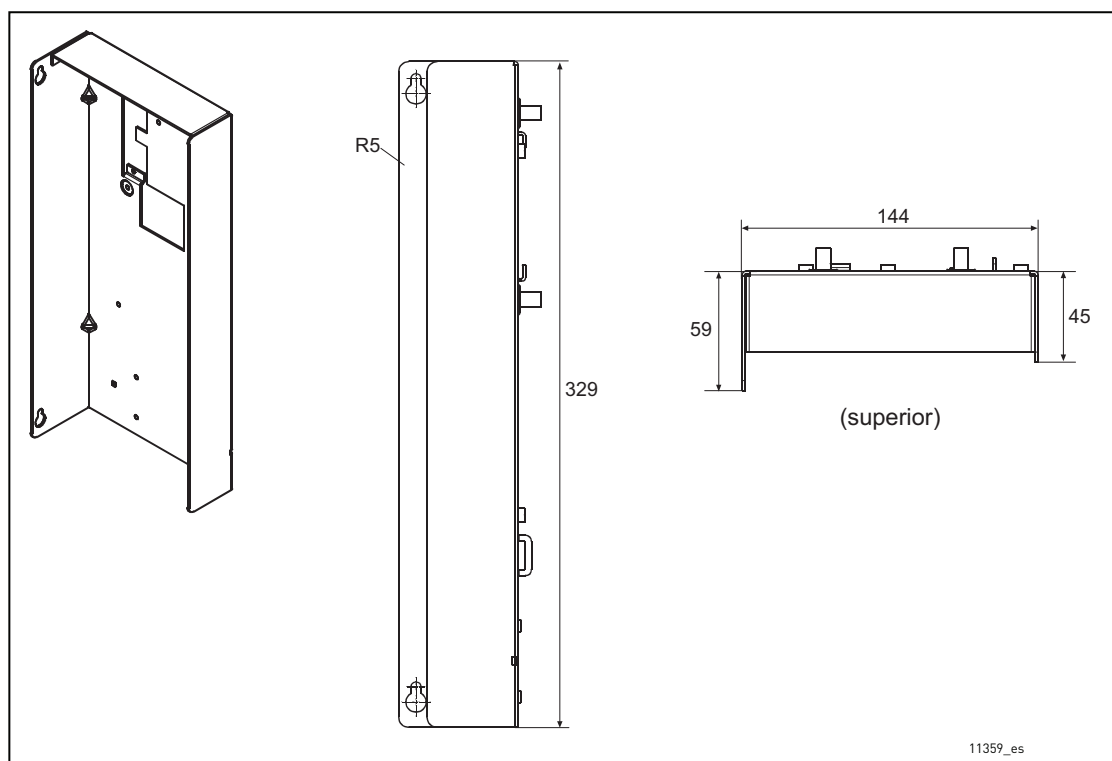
Dimensiones de la caja de montaje de la unidad de control
